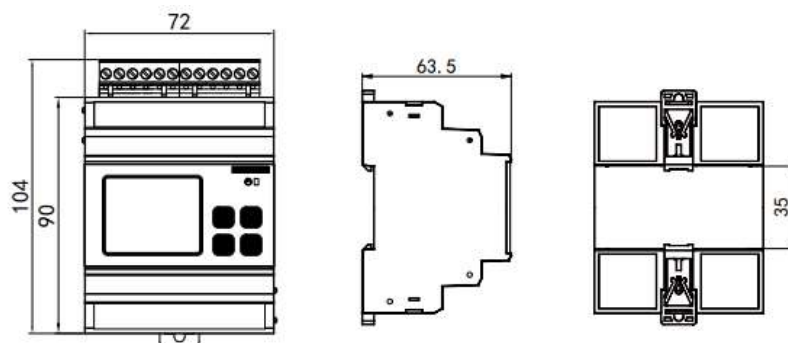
Внешний вид и габаритные размеры модуля измерительного КСМ-М1-1 и КСМ-М1-3
